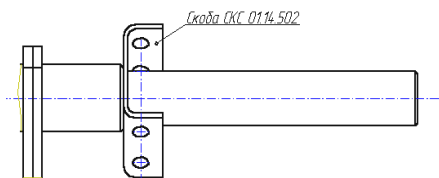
Скобу СКС 01.14.502 срезать по сварке.
